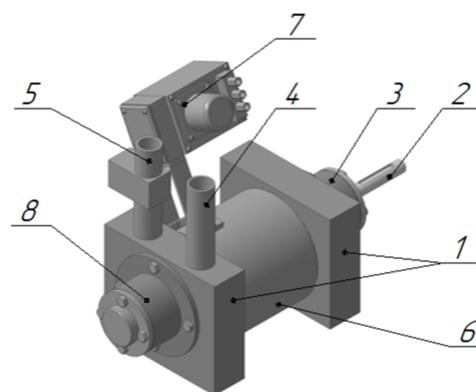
ЖВН с устройством автоматического регулирования нагнетательного окна: 1 – боковые стойки; 2 – вал; 3, 8 – подшипниковые опоры; 4 – патрубок впускной; 5 – патрубок выпускной; 6 – цилиндрический корпус; 7 – устройство автоматического регулирования нагнетательного окна
